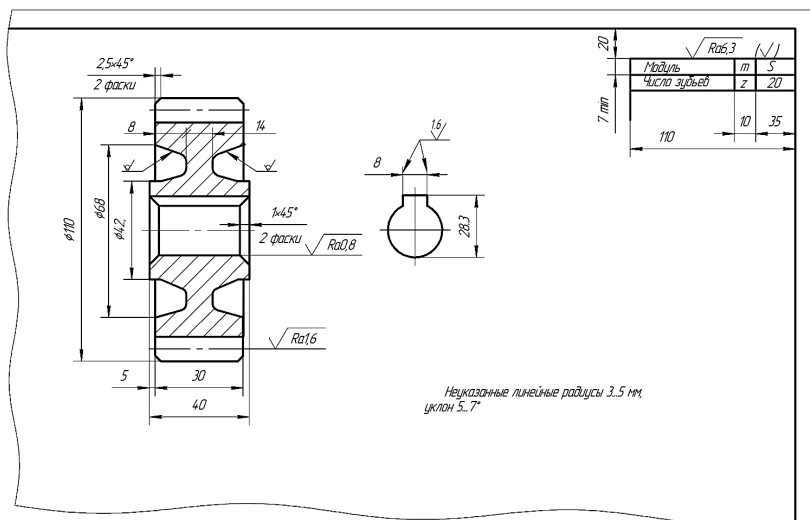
Цилиндрические зубчатые колеса и рейки
